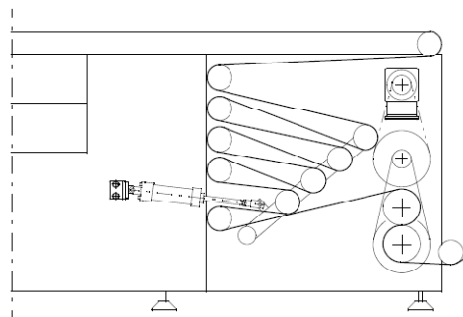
Rodillos de alimentación a las barras soldadoras.
